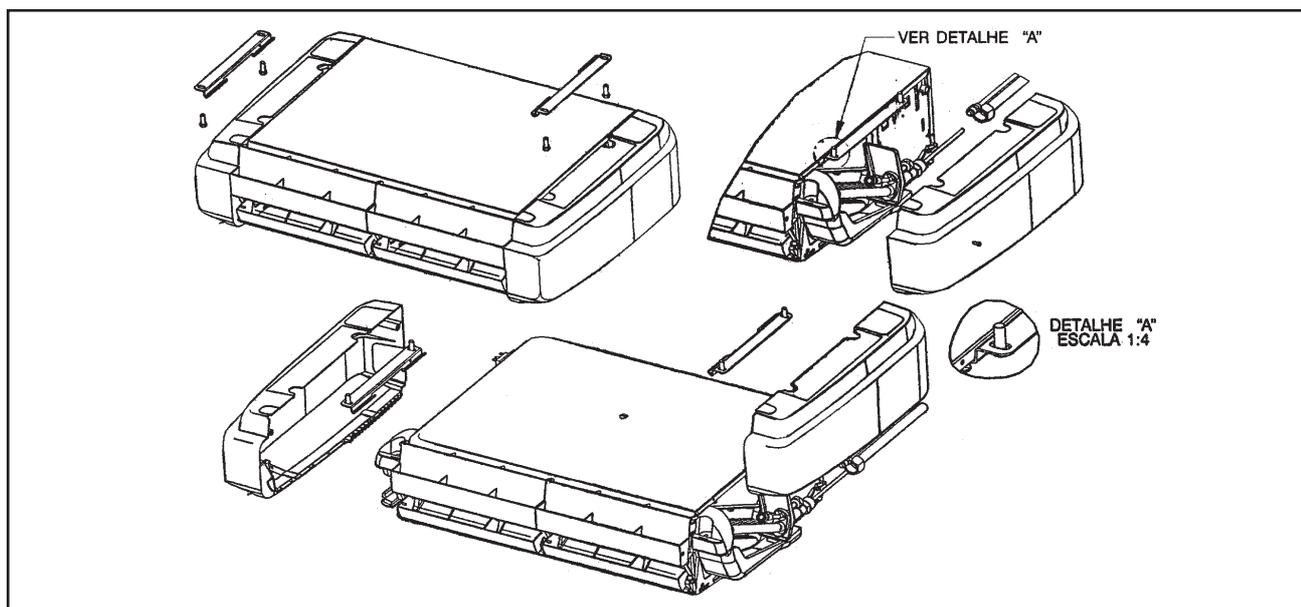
MONTAGEM DO SUPORTE DE FIXAÇÃO
